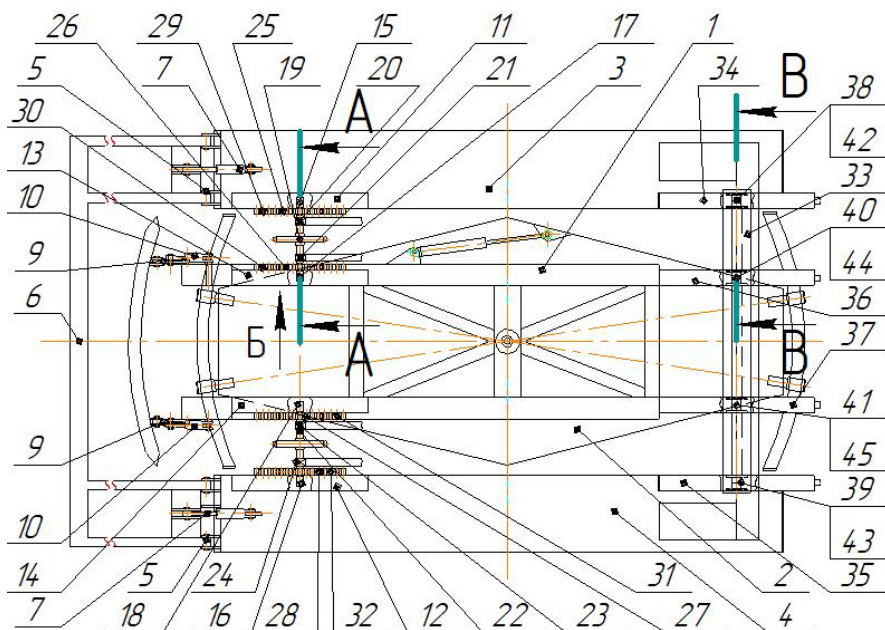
Шагающий болотный тягач, вид сверху (кабина не показана)
